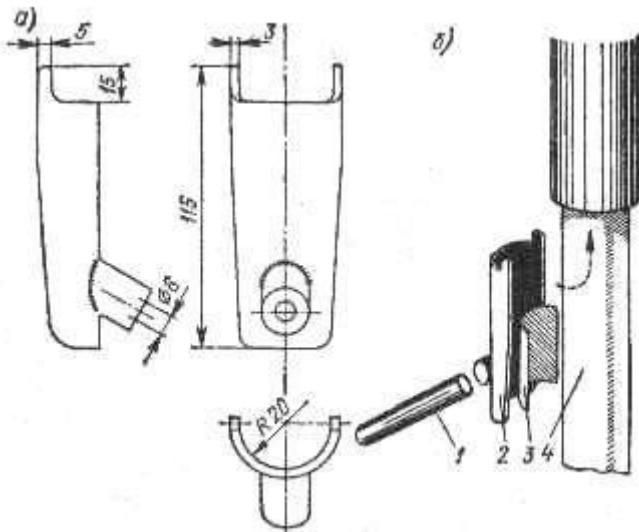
Приспособление для затяжки гайки-сальника пера передней вилки без его разборки:
